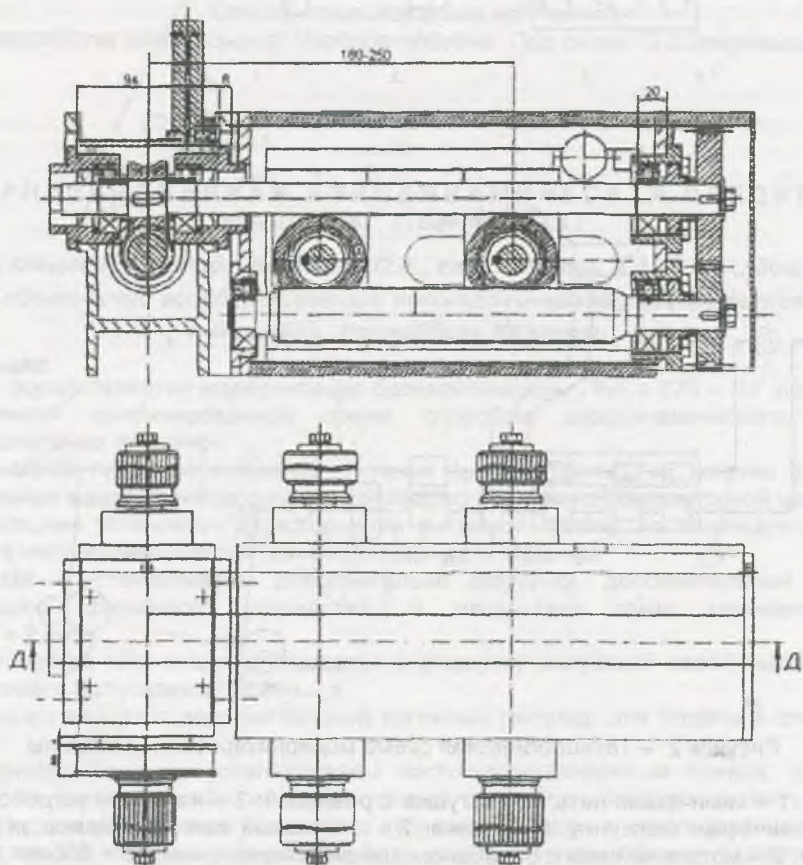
Передача вытяжного прибора предлагаемой конструкции
